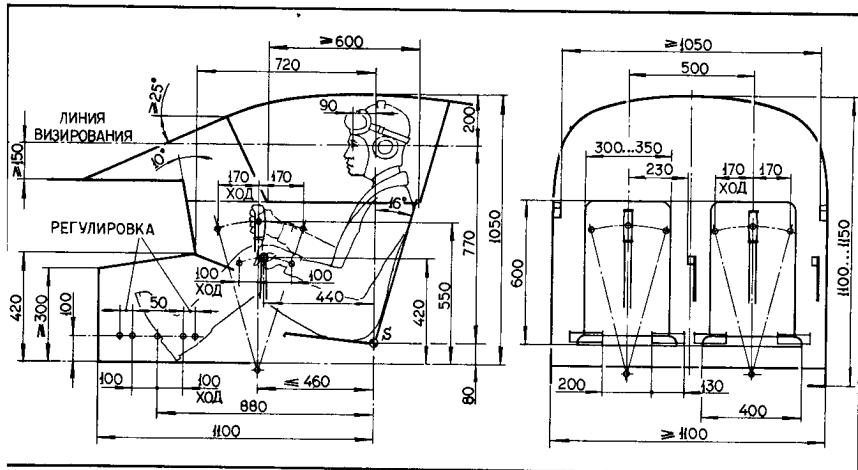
Рекомендуемые размеры кабины двухместного самолета с расположением членов экипажа бок о бок
